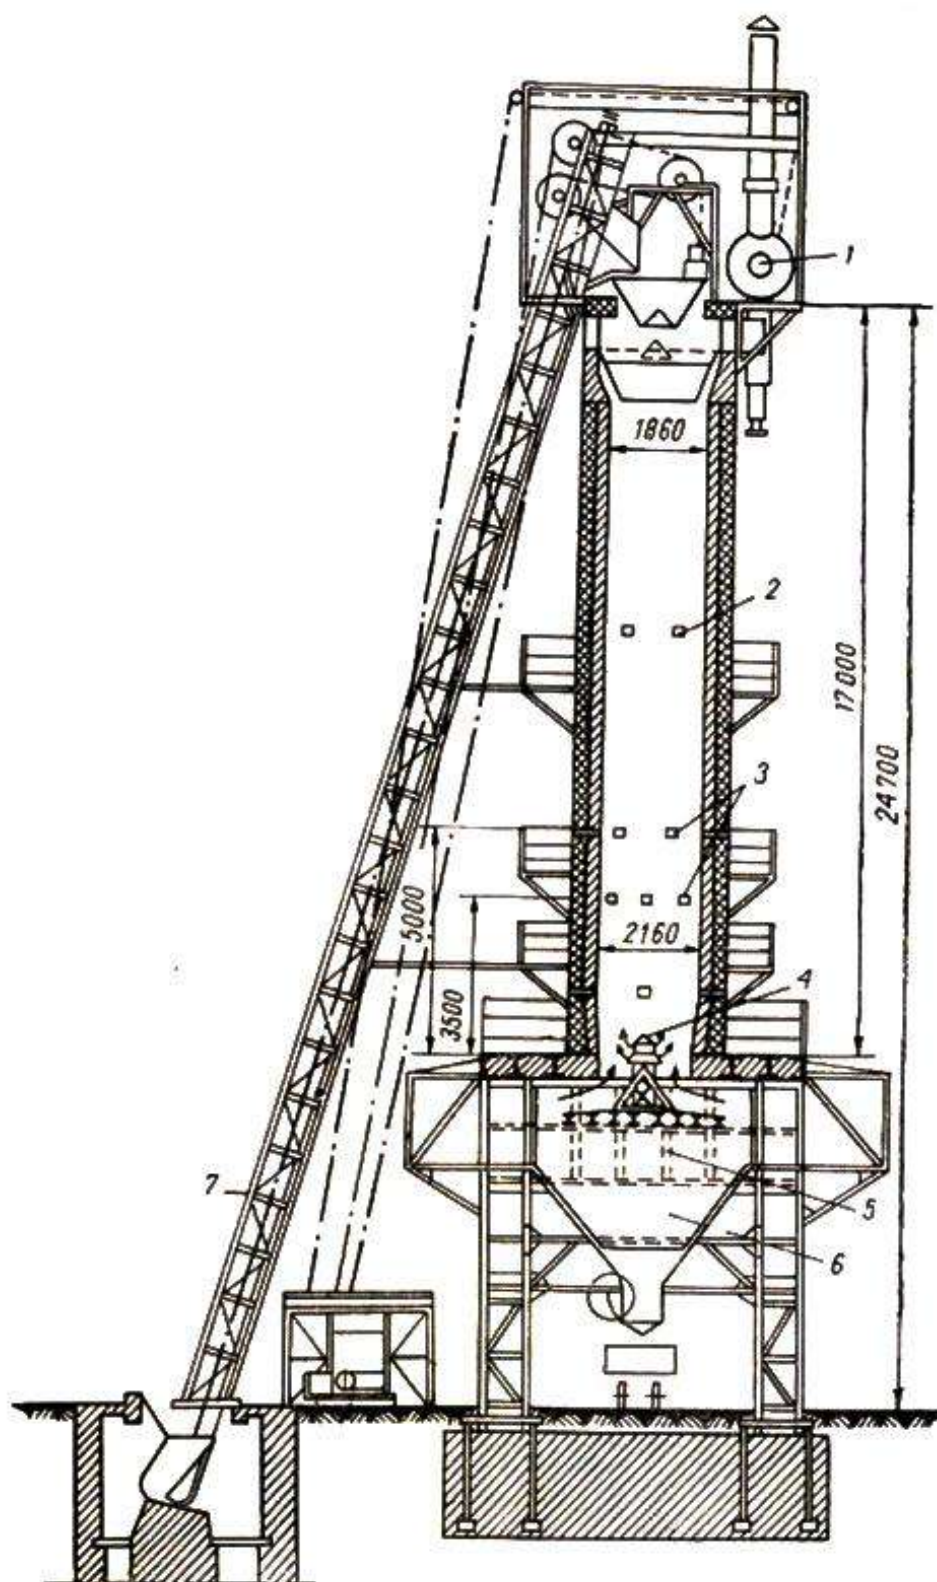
Вертикальная печь для обжига известняка: 1 – газодувка; 2 – смотровое отверстие; 3 – газовые горелки; 4 – горелка; 5 – воздуховод; 6 – бункер; 7 – элеватор
